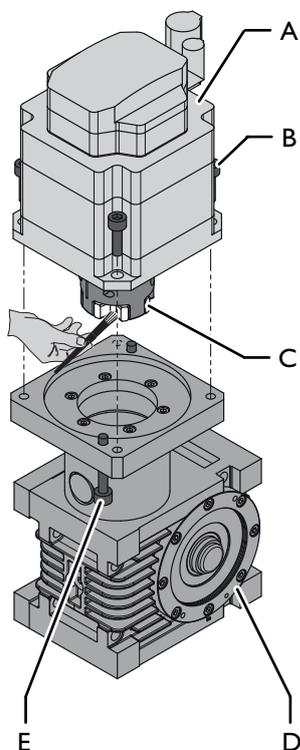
Смонтировать мотор: Блок редуктора Güdel
